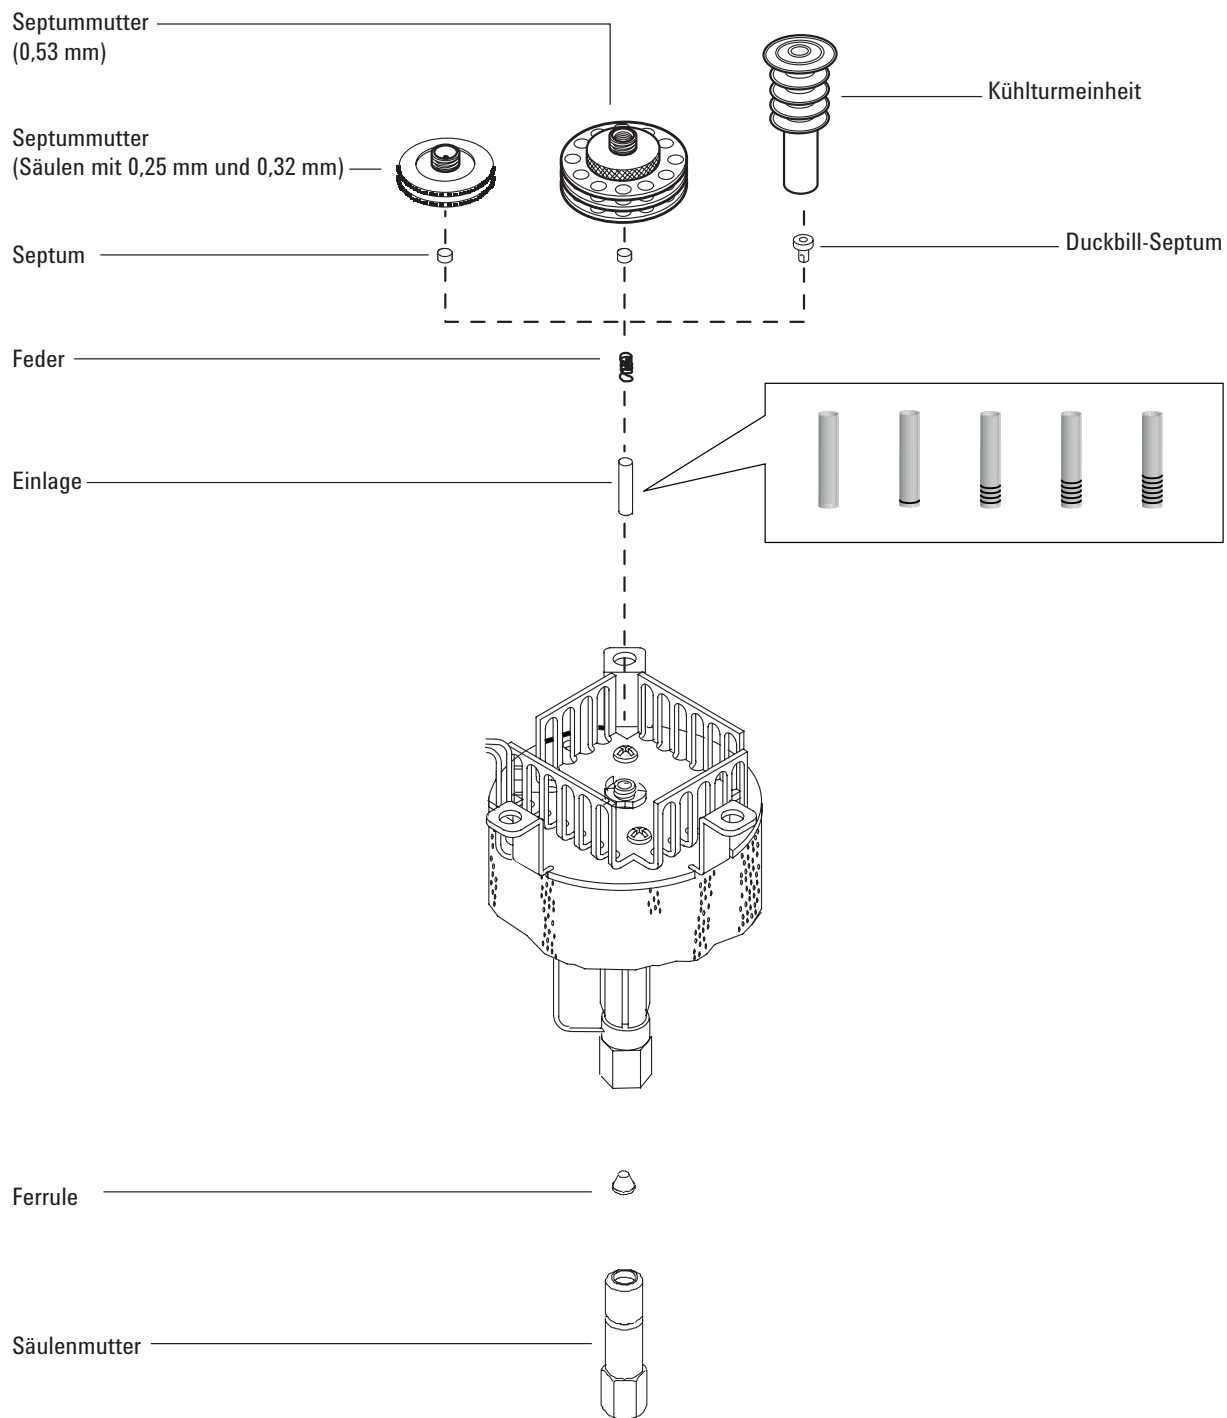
Explosionsansicht von Teilen des Kaltaufgabesystems
